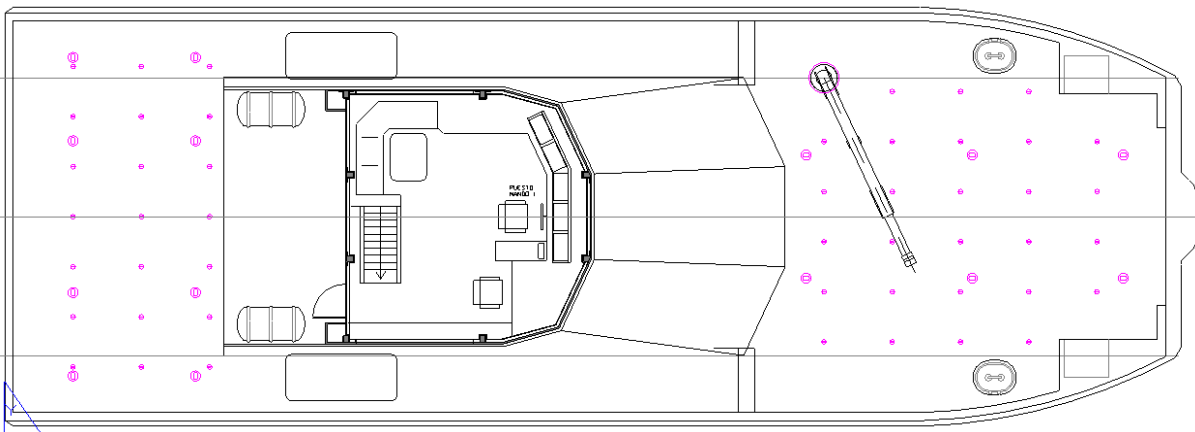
Vista en planta de la cubierta superior. Elaboración propia.
